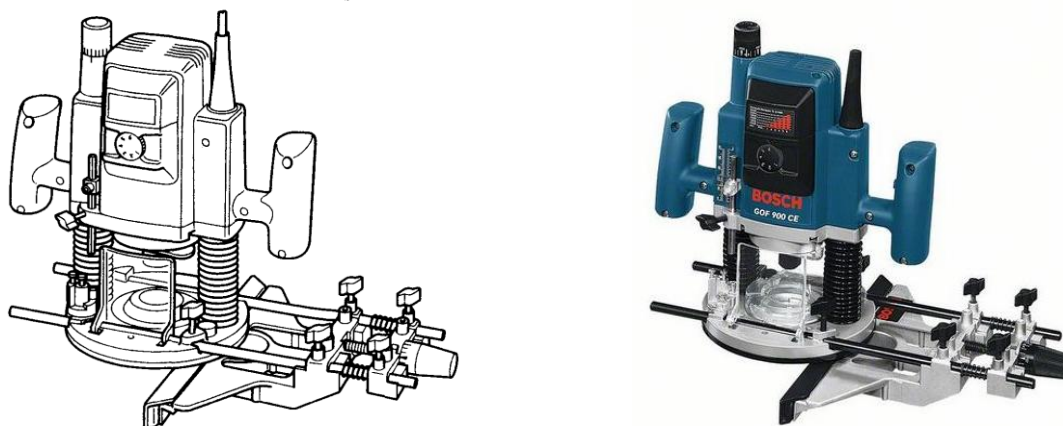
Вертикальная фрезерная машина GOF 900 CE
